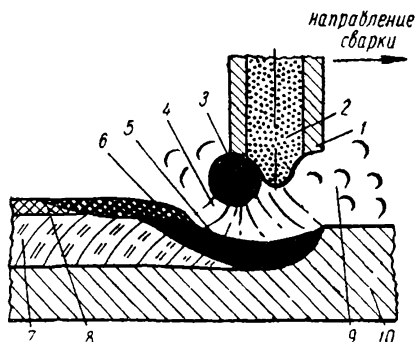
Схема процесса сварки самозащитной порошковой проволокой.
